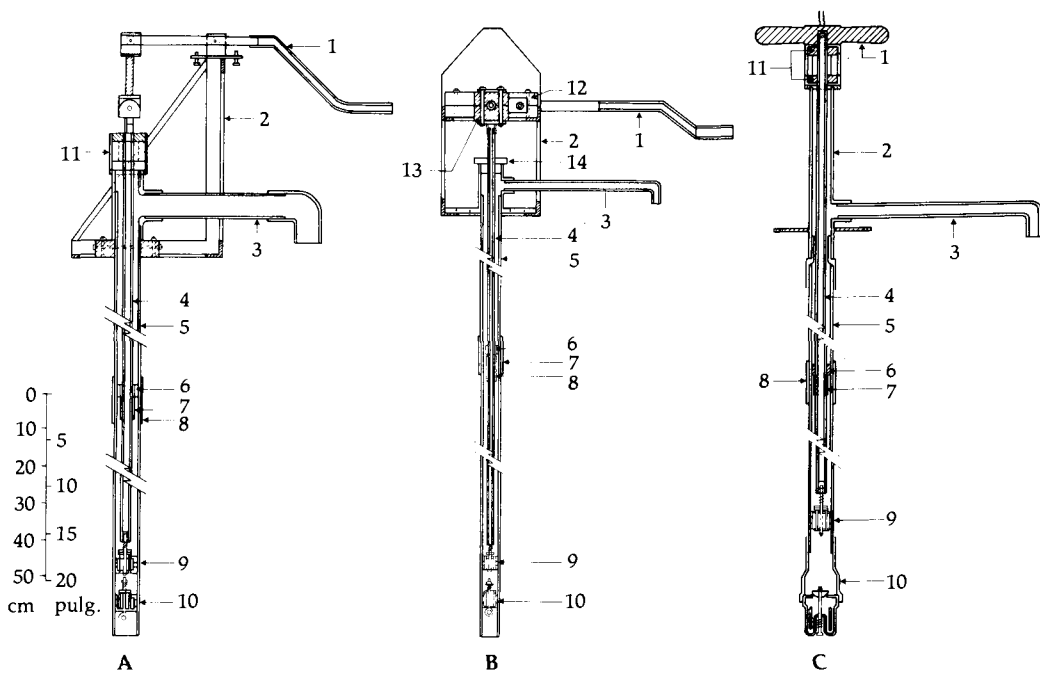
(A) bomba L1, (B) bomba L3, y (C) bomba V1: 1) manija, 2) estructura; 3) conducto; 4) varilla del pistón; 5) tubo de elevación; 6) guía de varilla del pistón; 7) unión de pistón; 8) unión del tubo de elevación; 9) pistón; 10) válvula de retención; 11) cojinete de madera y caja del contador (L1 y V1); 12) cojinete principal (L3); 13) cojinete de la cabeza (L3); y 14) base del contador (L3).
